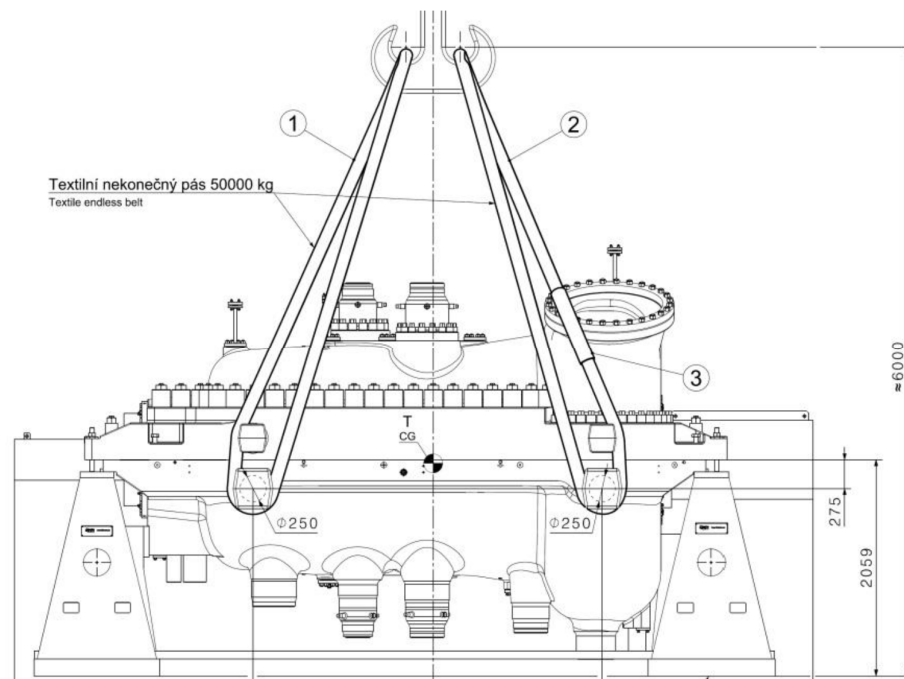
ESQUEMA DE IZAJE DE TURBINA
